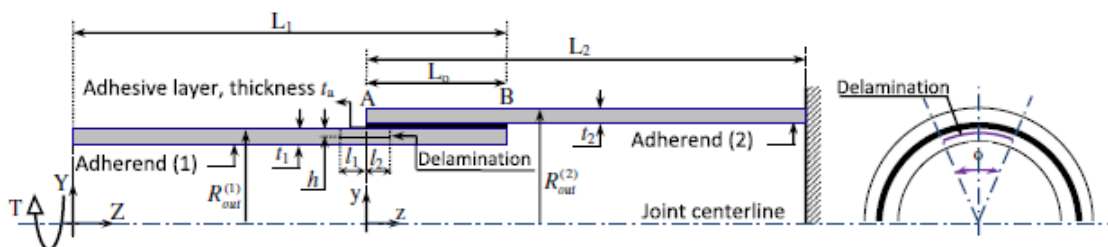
Dimensões básicas de junta de sobreposição simples [44].
